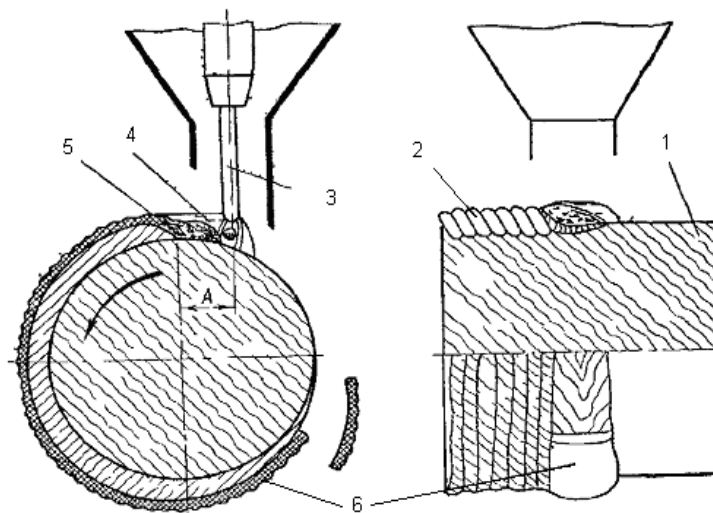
Схема наплавлення під шаром флюсу:
